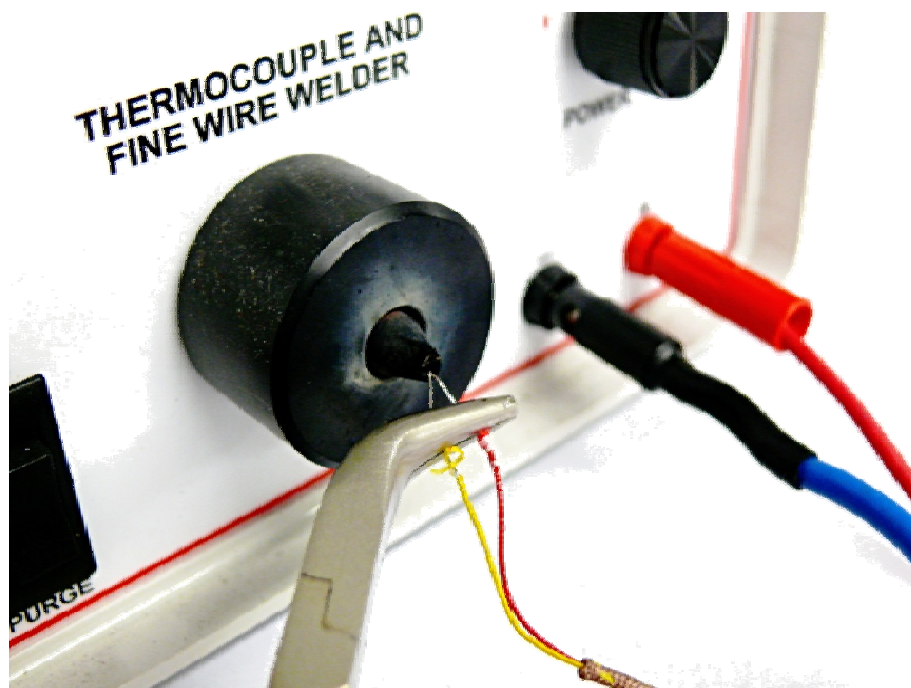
Svářečka termočlánekových drátů TL-WELD.
